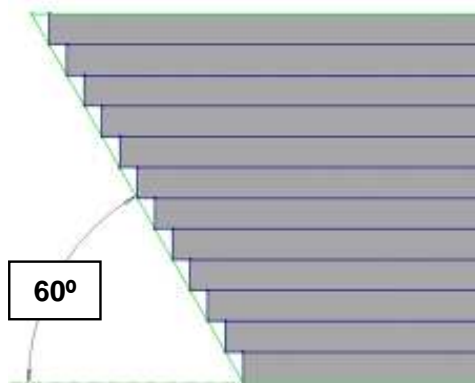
Imagen de plano inclinado a  $60^\circ$  fabricado por capas en SLM.
